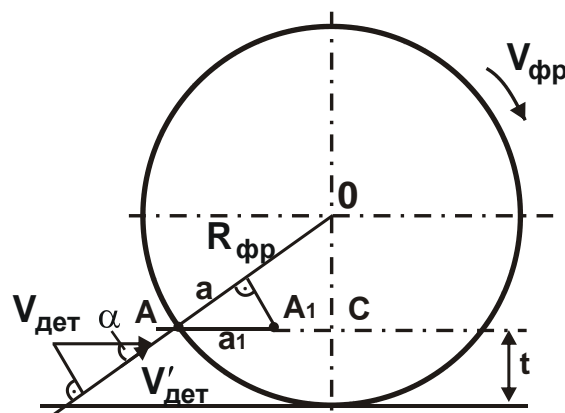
Розрахункова схема параметрів фрезерування циліндричною фрезою
